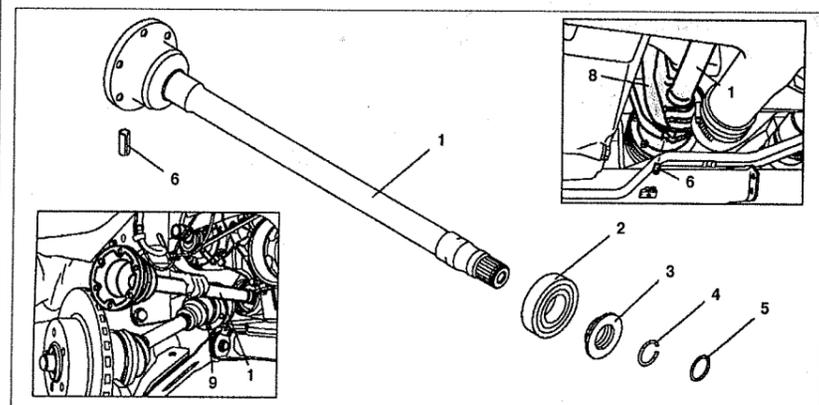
Центральный ведущий вал с подшипником (автомобили с двигателями 111.948 и 601.970):
